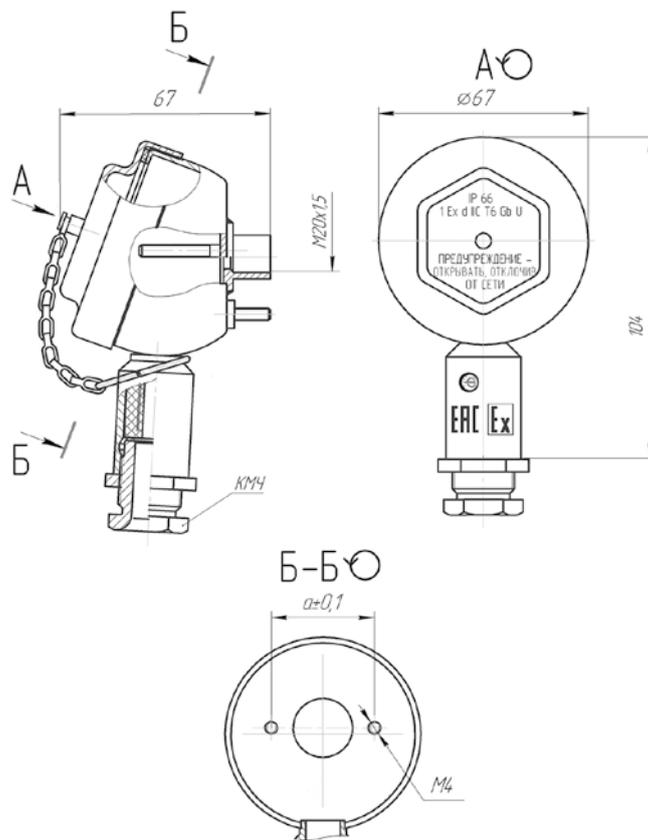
Габаритный чертеж головки соединительной с одним кабельным вводом
